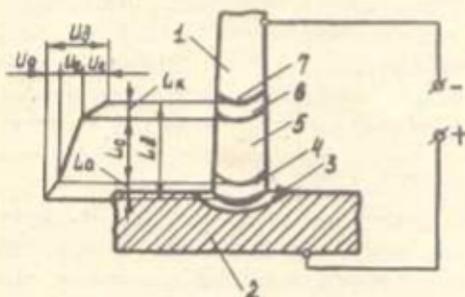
Схема сварочной дуги и падения напряжения в ней:
